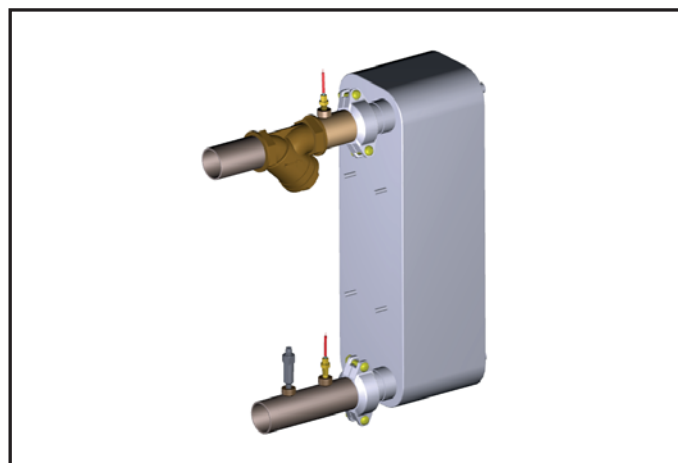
Kit de Conexão Solda-Victaulic com Filtro Y;
